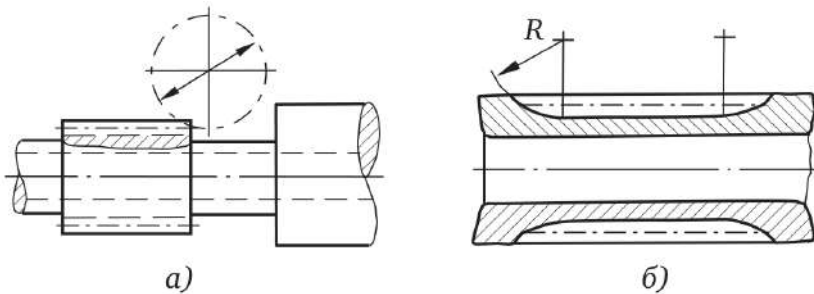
Форми деталей, що забезпечують вільний вихід інструменту
